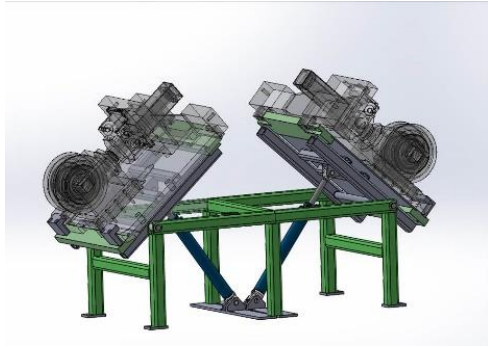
Suporte de montagem do bloco superior da zona de soldadura
